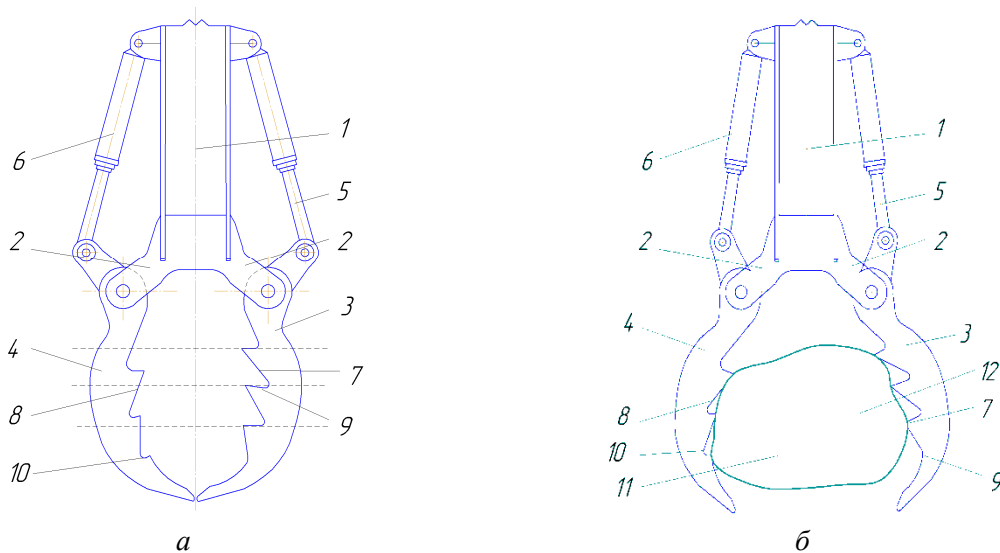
Робочий орган захвата із ребристими асиметричними зубцями:
